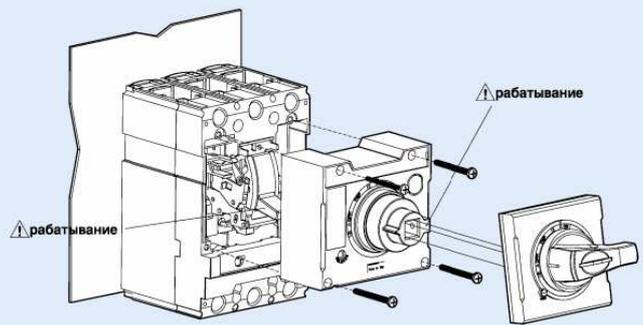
Габаритные и установочные размеры, способ установки выносных поворотных рукояток TS100, TS160 и TS250
